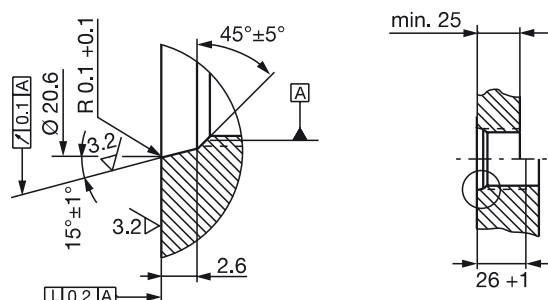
Einschraubloch 3/4"-16UNF nach SAE J475 O-Ring 15.3×2.4
